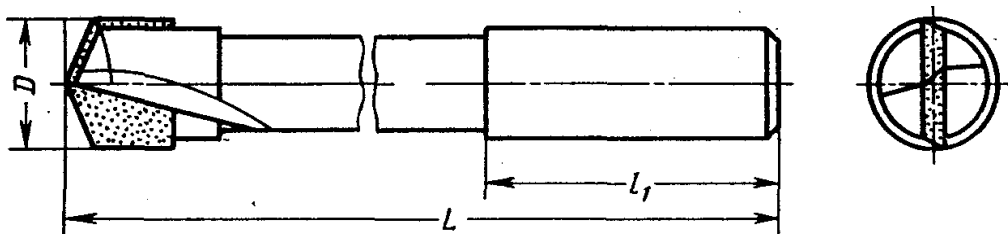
Свердло з припаяною пластинкою з твердого сплаву
